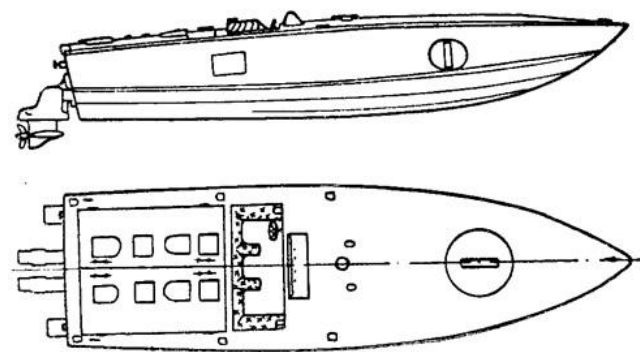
Гоночный катер Cigarette. Общее расположение [2].
